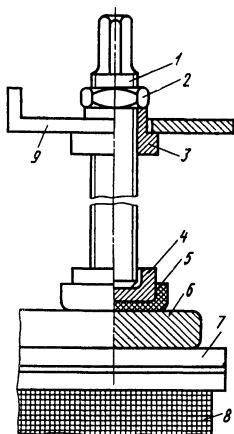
Схема прессовки обмоток кольцами и нажимными винтами
